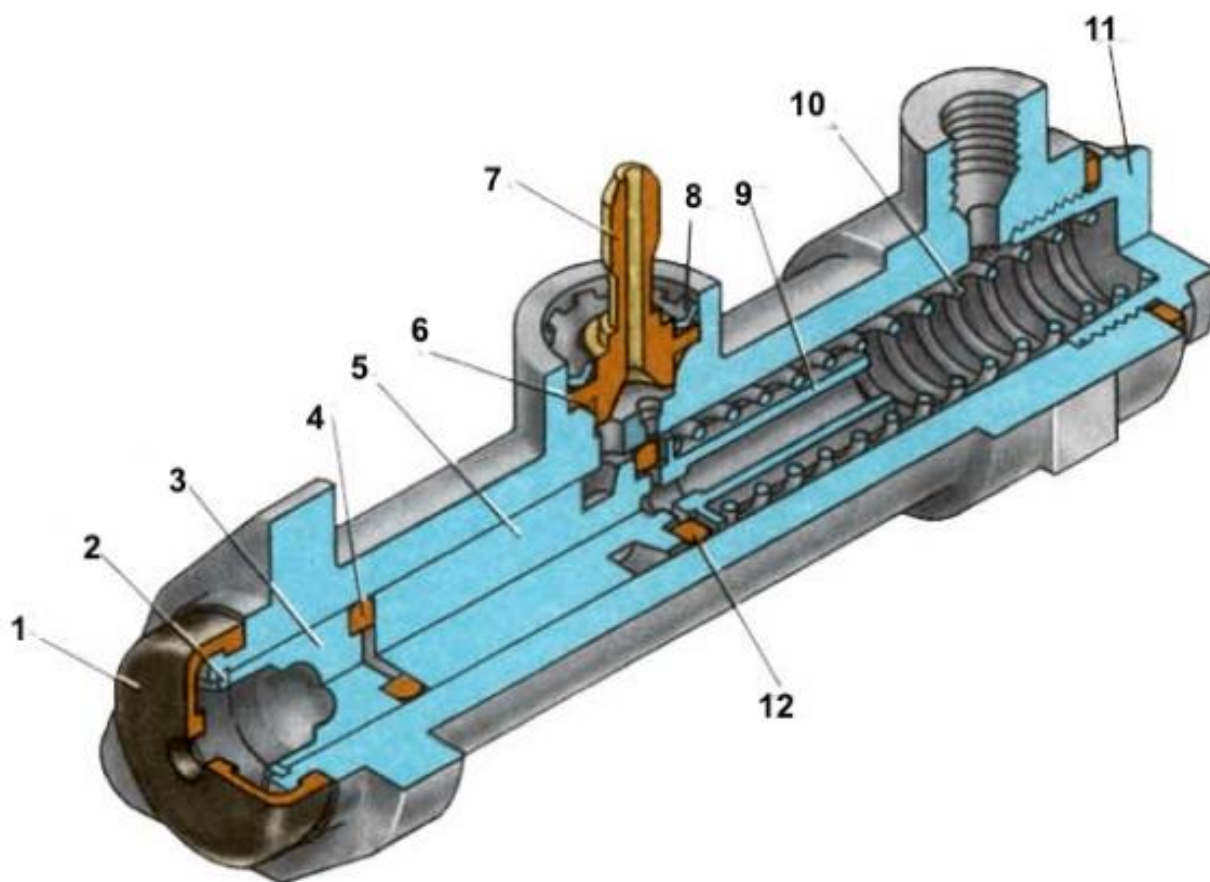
Главный цилиндр сцепления ВАЗ 2107:
